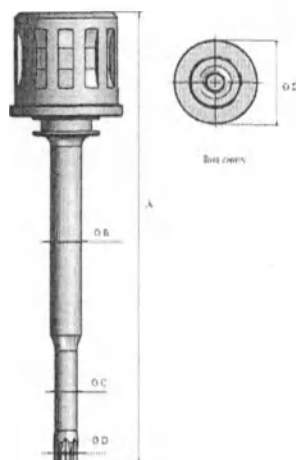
Схема отвертки звездчатые для динамометрического ключа
